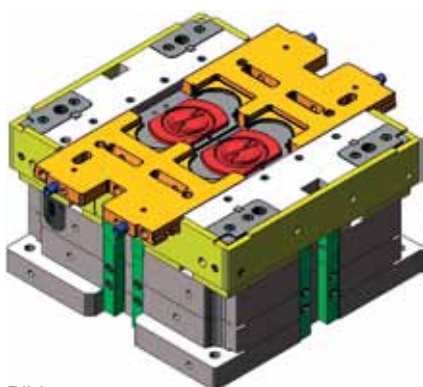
IsoForm®-Werkzeug mit Schiebern (180 °C)
